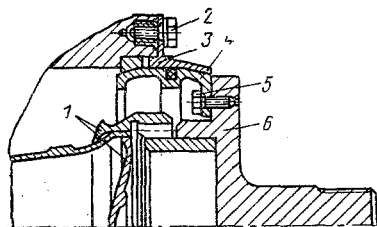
Схема присоединения транспортировочного фланца к двигателю:
